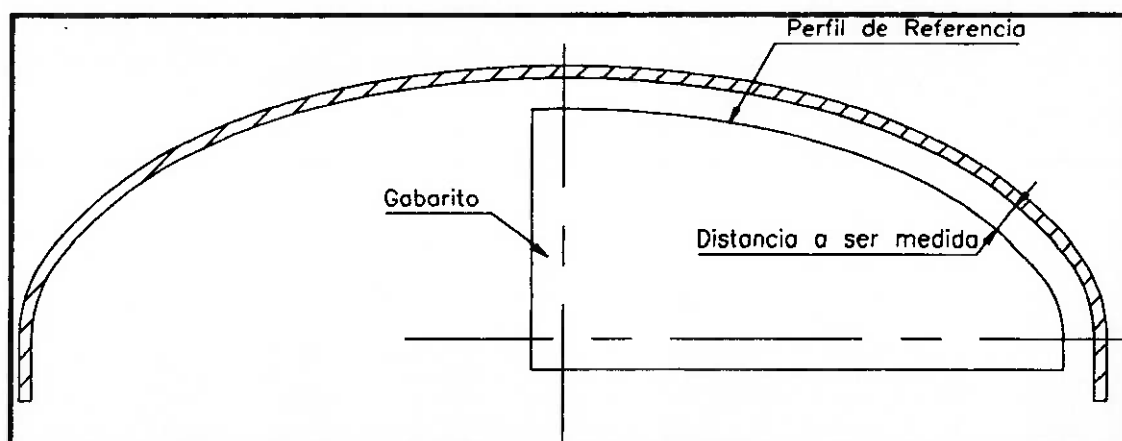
Inspeção dimensional do tampo após conformação
